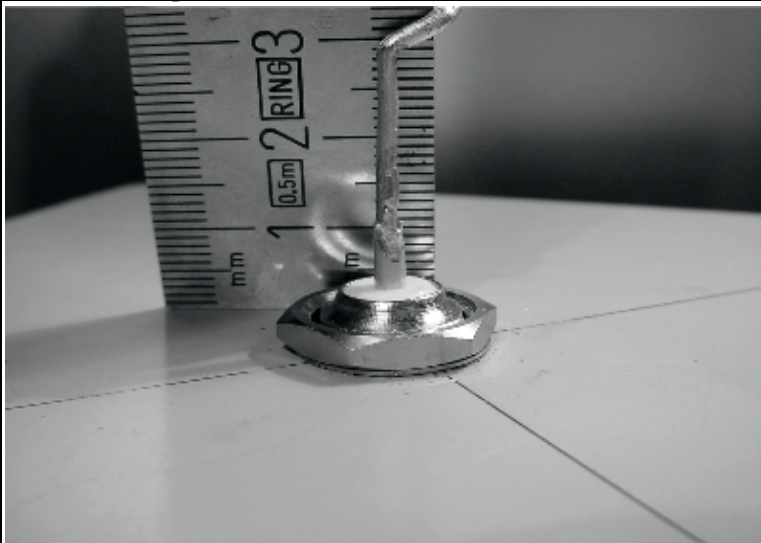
Fissare strettamente il connettore N alla piastra.
